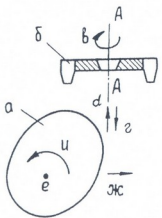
Схема нарезания арочных зубьев некруглого цилиндрического колеса
